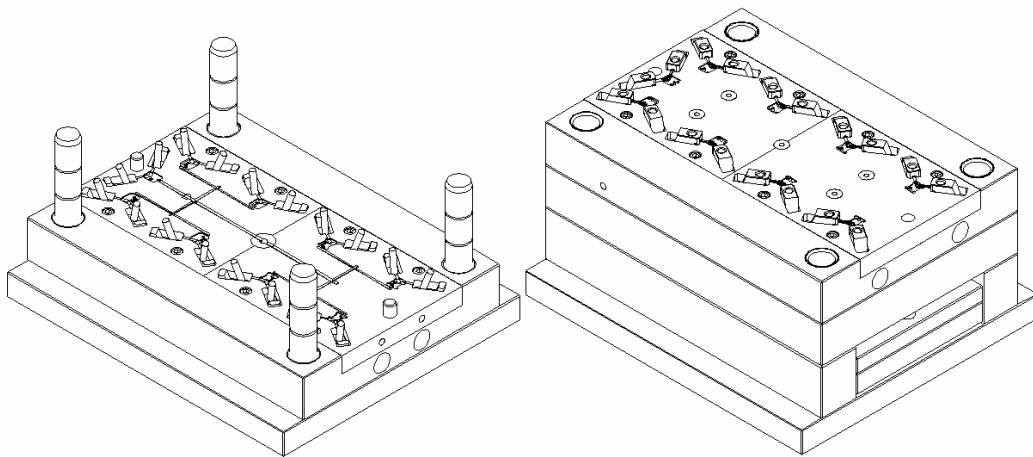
Molde para injetar a unidade representativa dos grupamentos amina e carboxila: vista isométrica em escala reduzida mostrando as duas partes do mesmo molde
